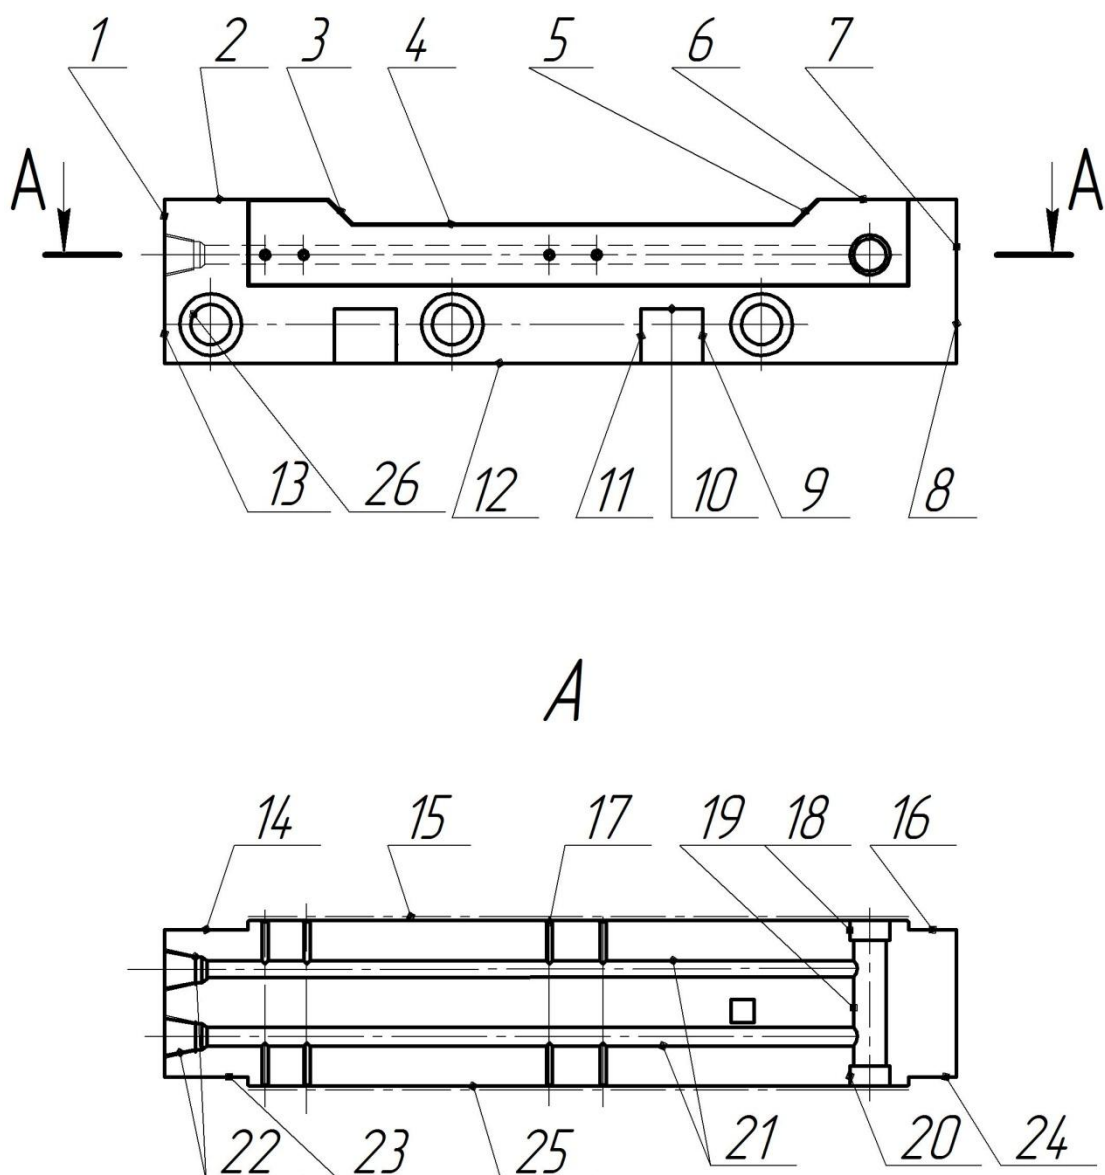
Деталь - «Корпус подшипников», общий вид
